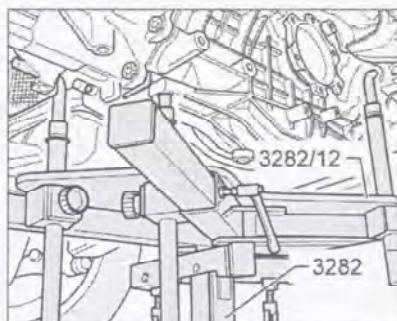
Закрепите приспособление приспособления для крепления коробки передач 3282 с выверочной доской 3282/10 на подъемнике и установите последний под коробку передач.
